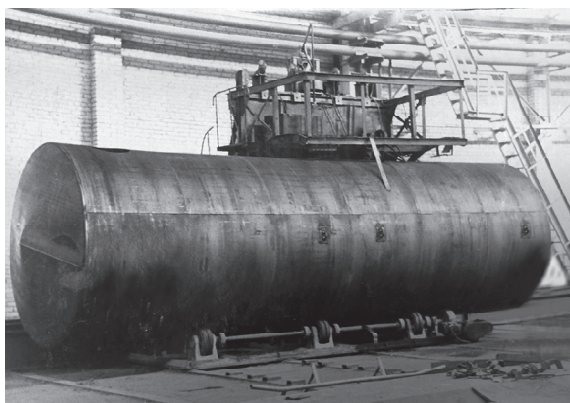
Схема стенда автоматической сварки горизонтальных резервуаров
